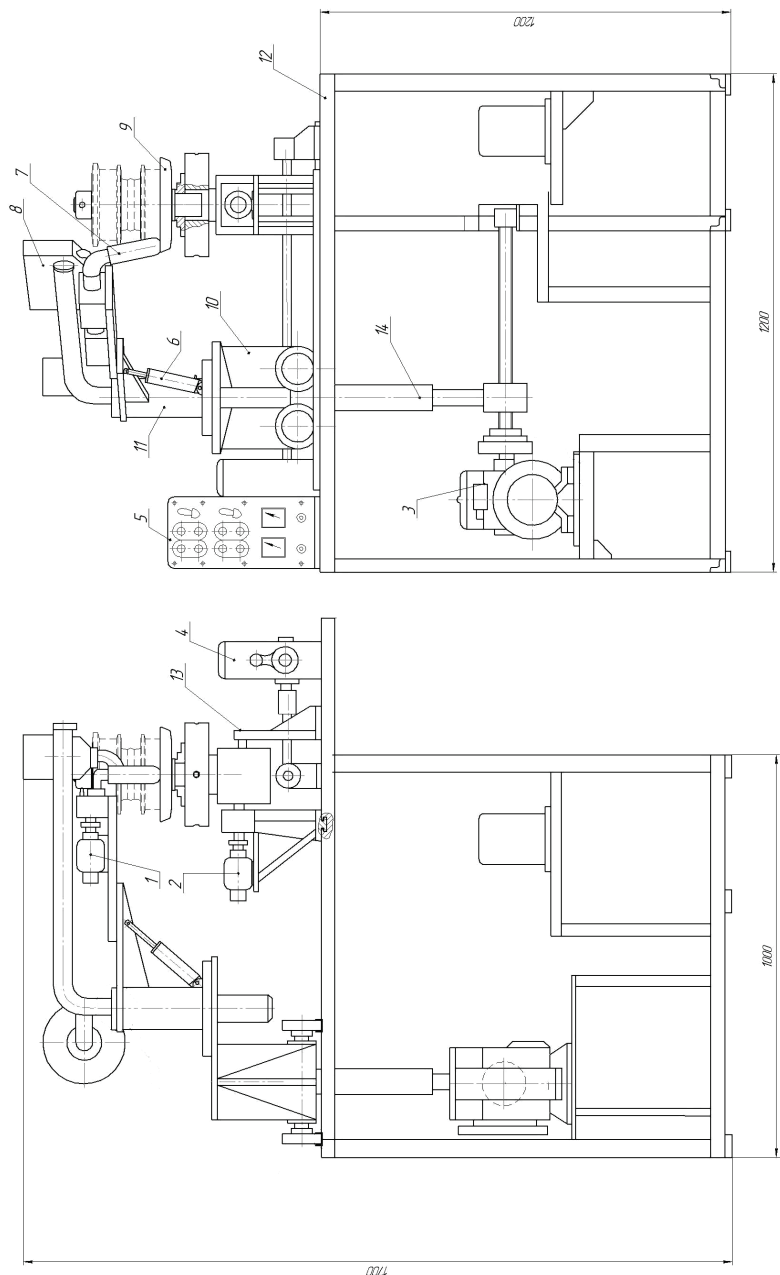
Установка для наплавки крупногабаритных деталей (обозначение в тексте)
